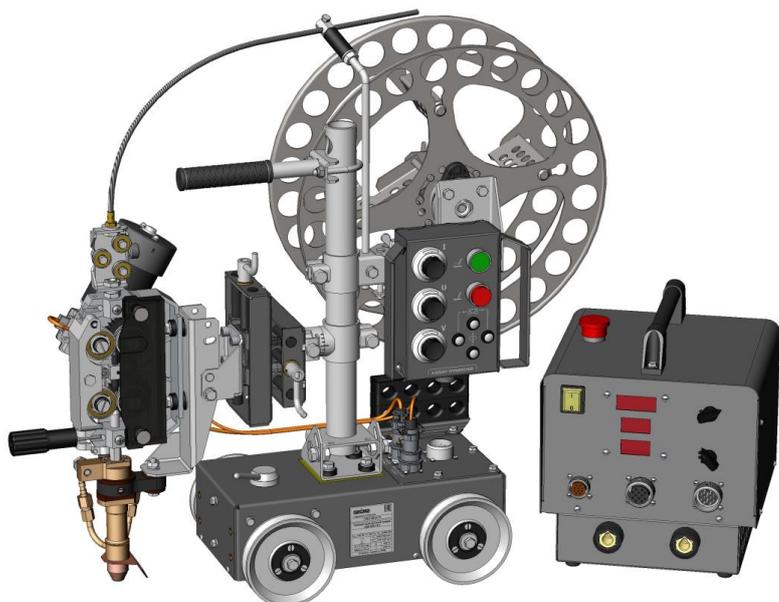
Автомат сварочный АДГ-630 исп.00 (базовое исполнение, с БУ-21). Код927И.
